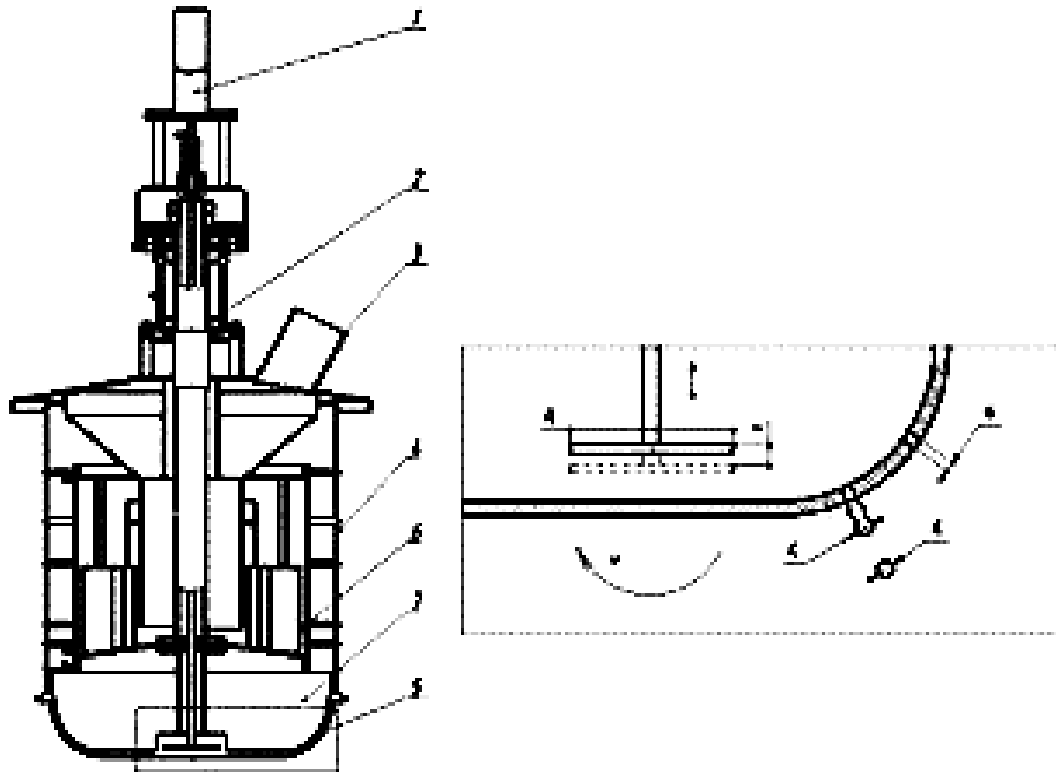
Конструкція ОВГ: 1 – вібраційний пристрій; 2 – підшипники; 3 – патрубок для входу плаву; 4 – корпус; 5 – перфорована корзина; 6 – розподільник; 7 – додаткові лопатки
